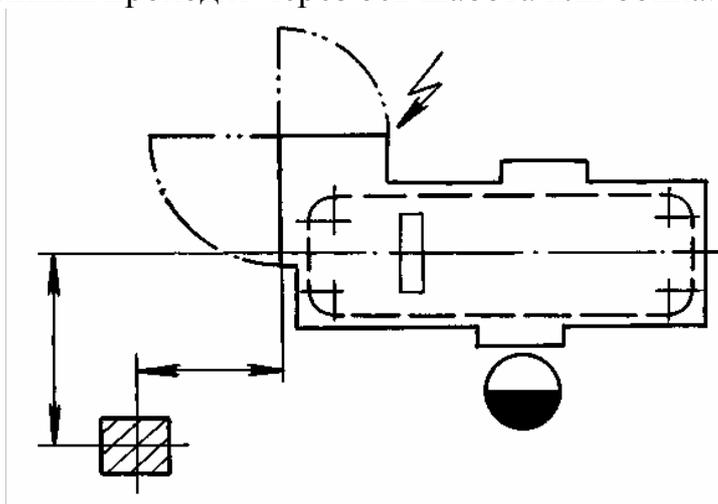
Привязка токарного станка 16K20 к элементам здания
